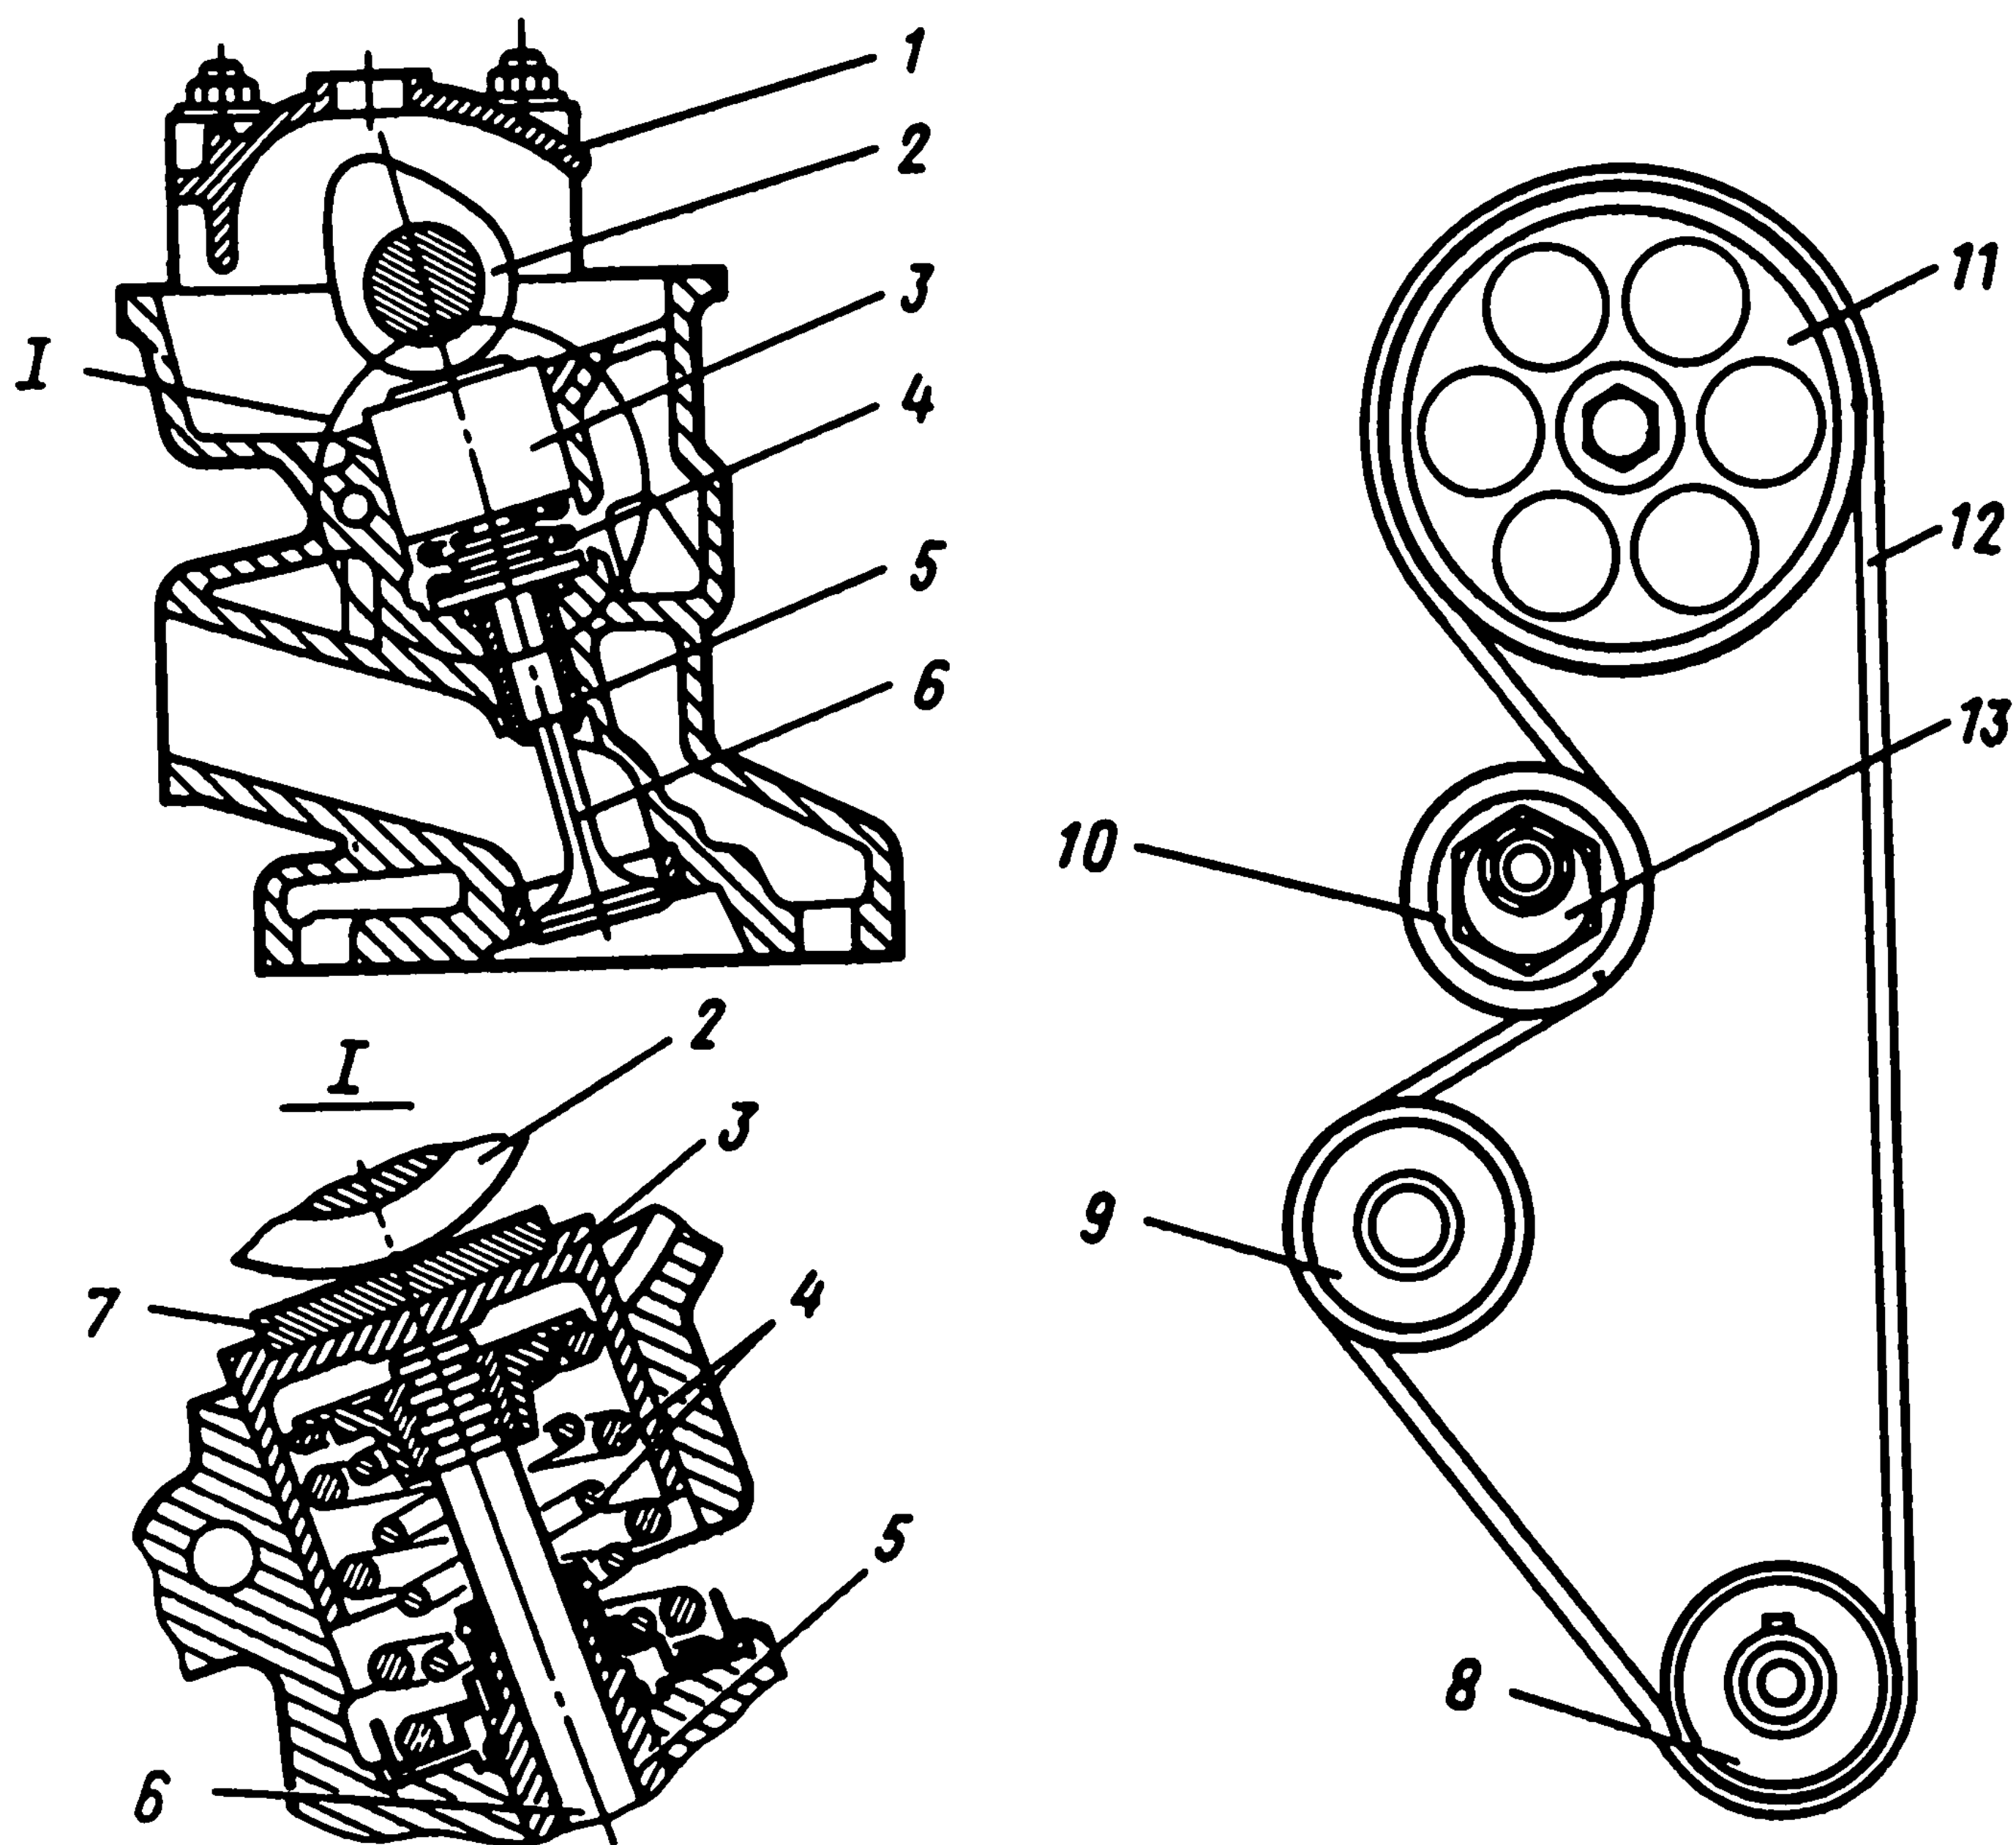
Газораспределительный механизм двигателя ВАЗ-2108
